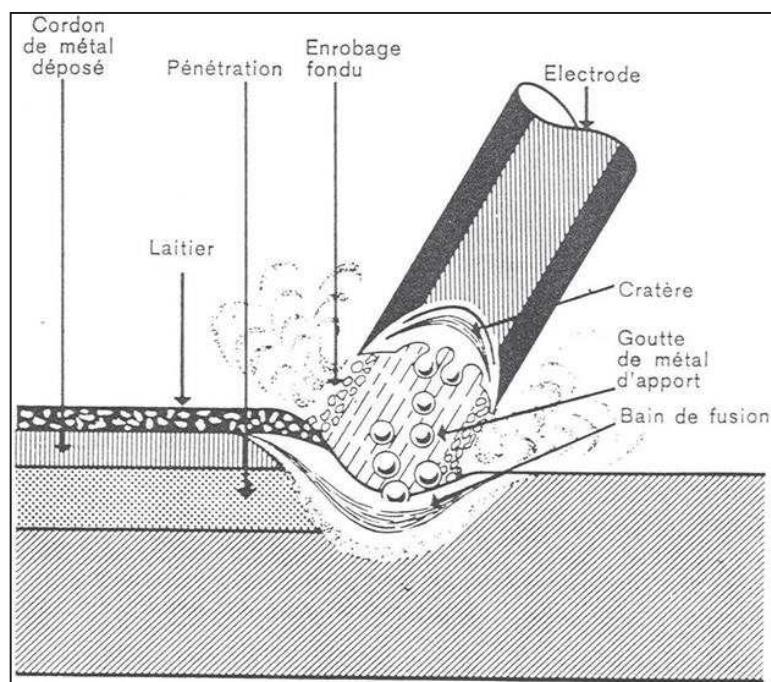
Schéma du mécanisme de soudage avec électrode enrobée [3]
